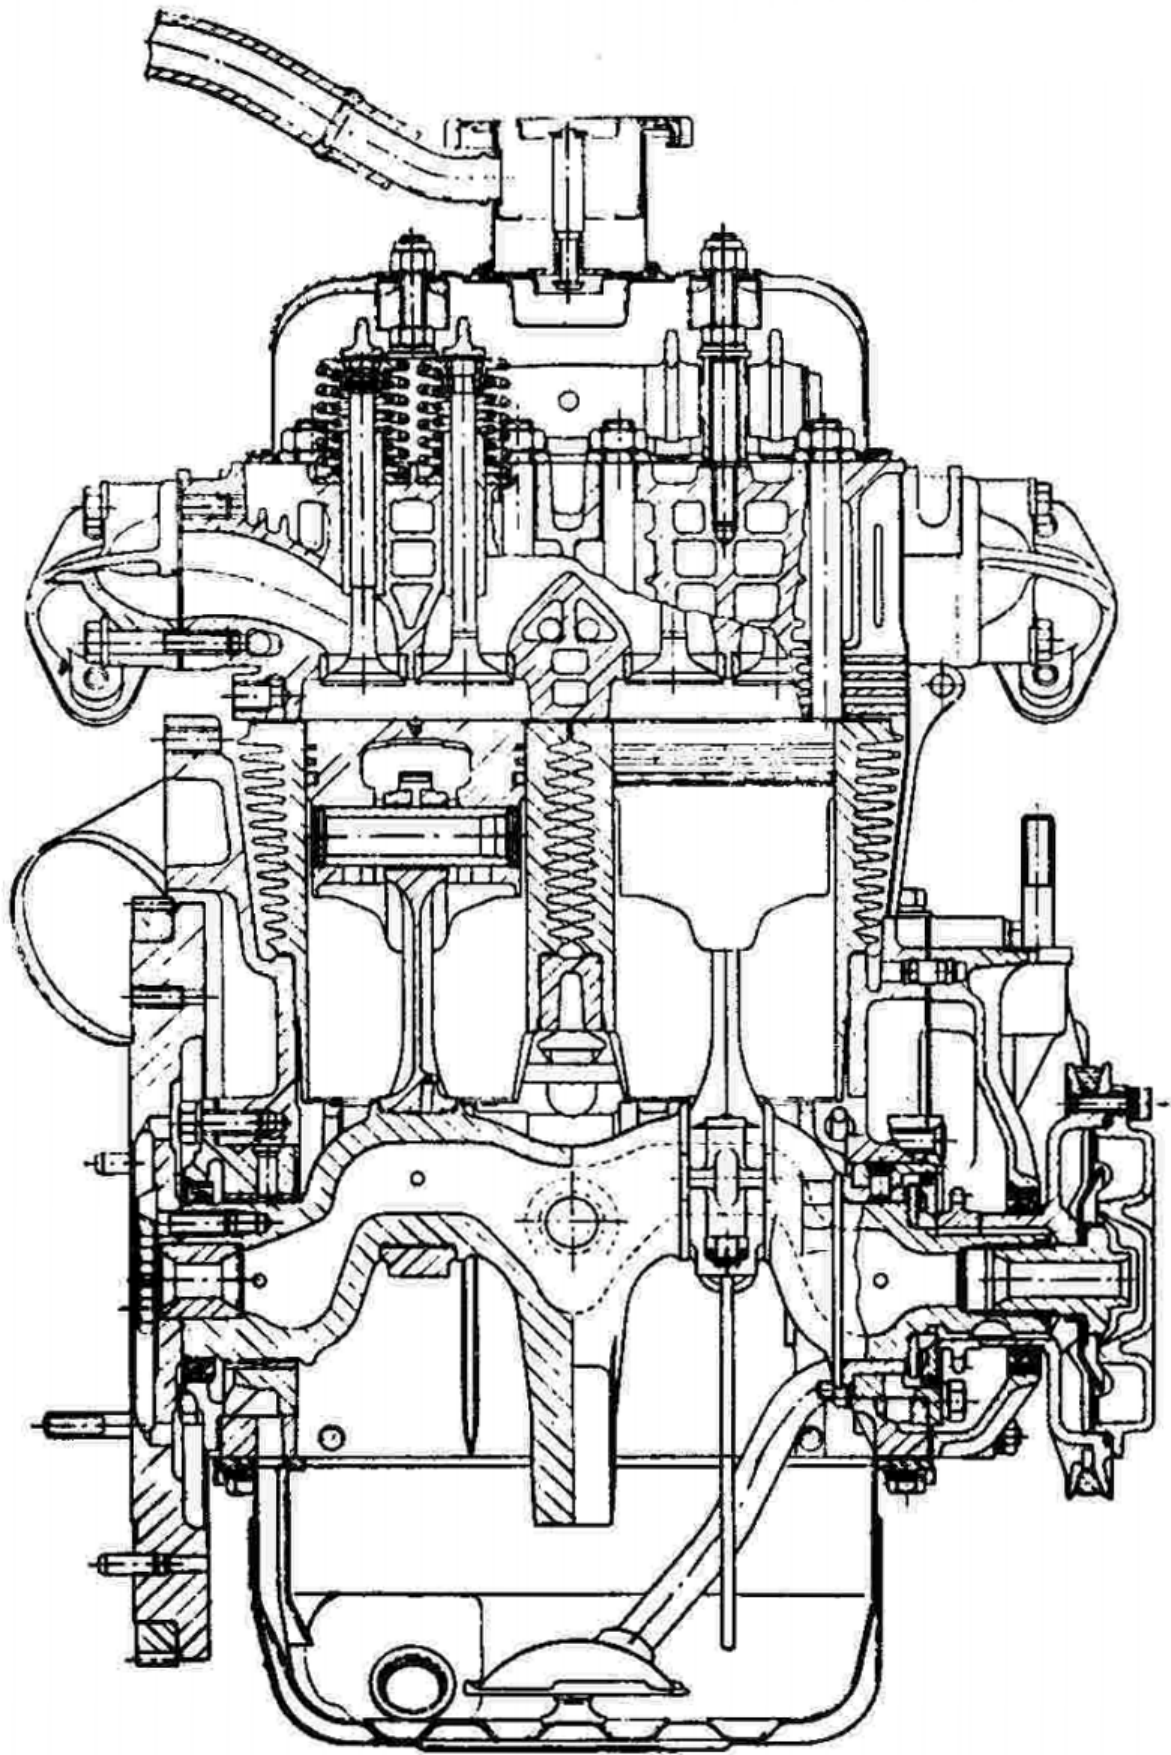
Pohled na motor Polski Fiat 126 P
